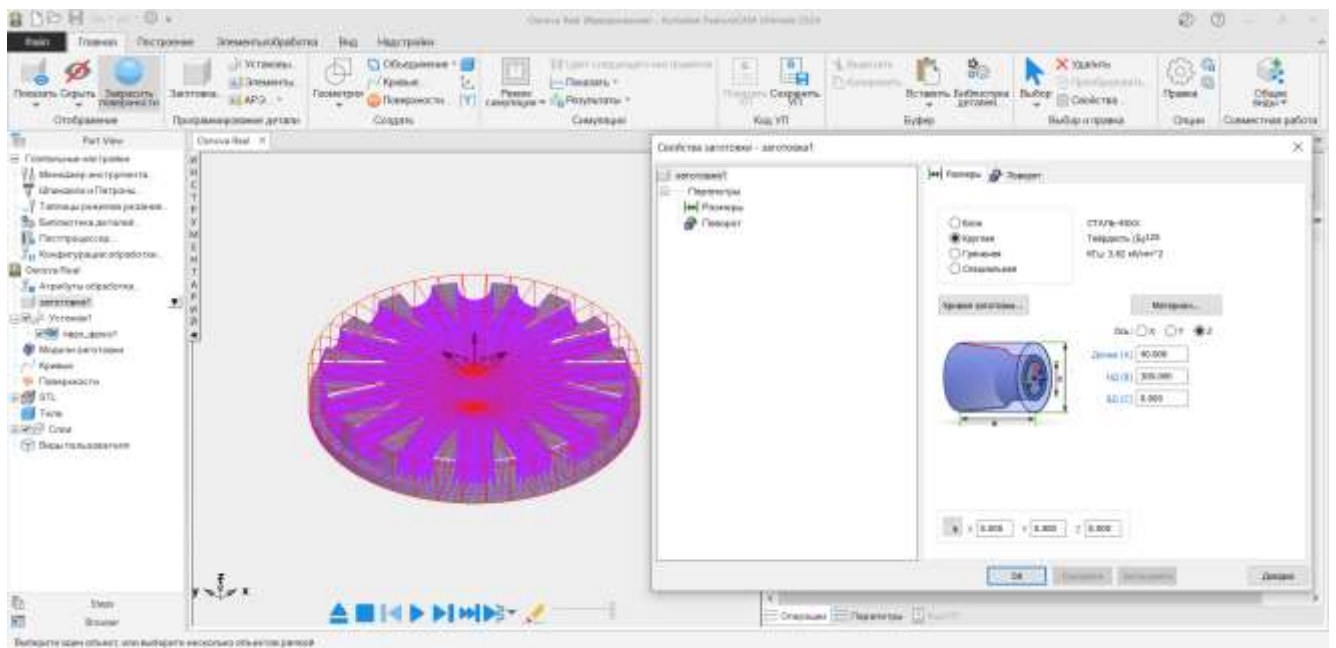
Налаштування форми та розміру заготовки.
